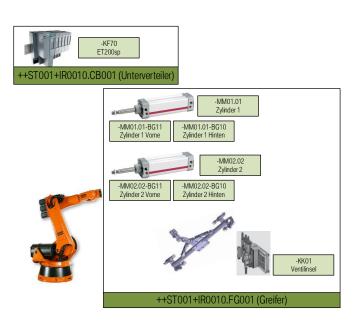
Anlagenkennzeichnungssystem: Detaillierte Betriebsmittelkennzeichnung
